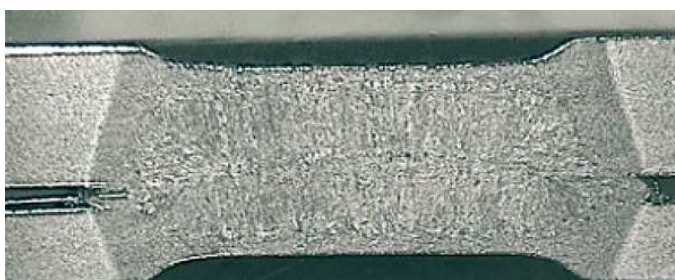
Soldadura homogénea Usibor® + Usibor®
